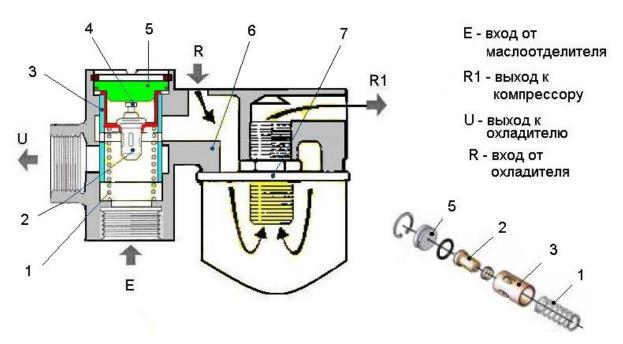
Схема потоков масла через клапан – термостат: 1 – пружина 2 - термоэлемент; 3 - стакан; 4 – шток; 5 – заглушка; 6 – корпус гидроплиты; 7 – фильтр масляный.
